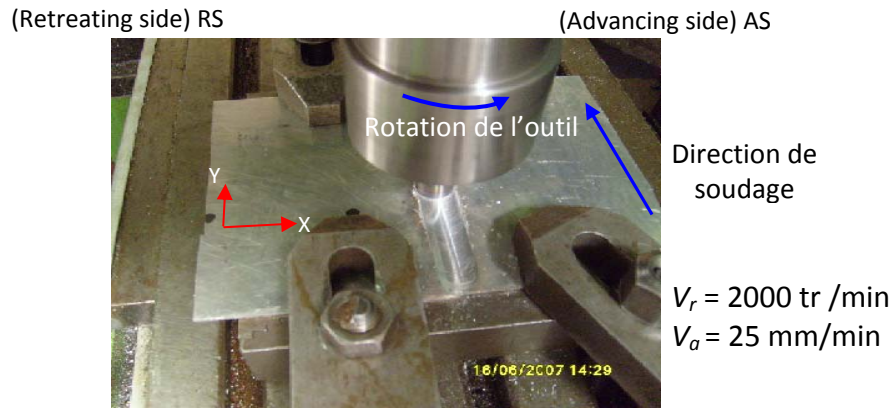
Soudure de 7075-T6 sans défaut (au cours du soudage).
